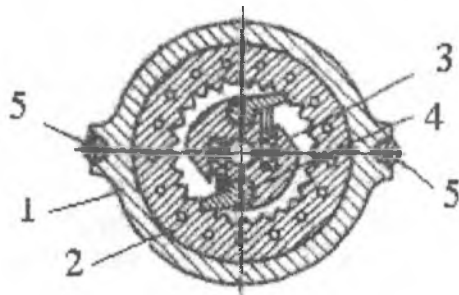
Поворотный механизм с двумя собачками в корпусе:
